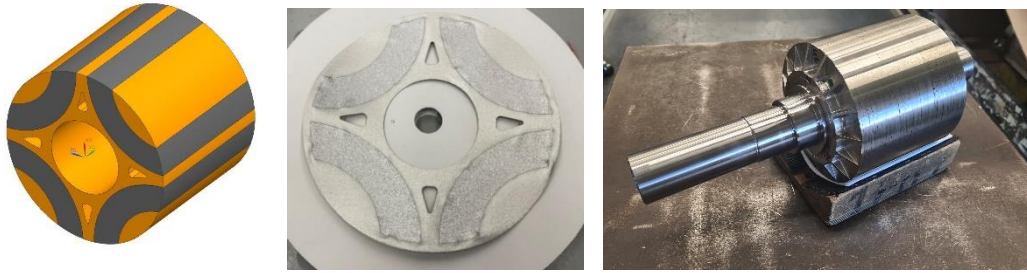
Hybriddruck des 2k-Rotorblechs im finalen Reluktanz-Design und Aufbau des Rotors (links: CAD-Design, Mitte: 2K-Einzelblech, rechts: final aufgebauter Rotor mit Welle)
